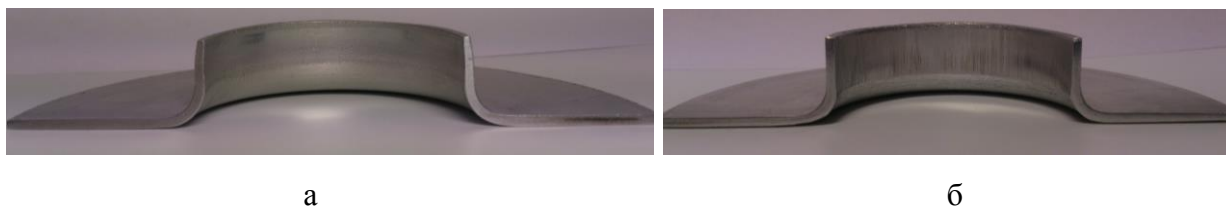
Здеформовані заготовки в розрізі, які отримані відбортуванням: а – традиційної заготовки, б – зпрофільованої заготовки
